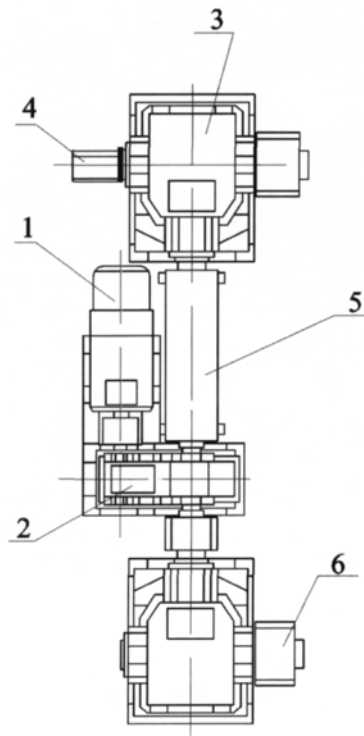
Схема приводу механізму підйому (існуючого): 1 – електродвигун; 2 – циліндричний редуктор; 3 – конічний редуктор; 4 – командоапарат; 5 – промвал; 6 – муфта
